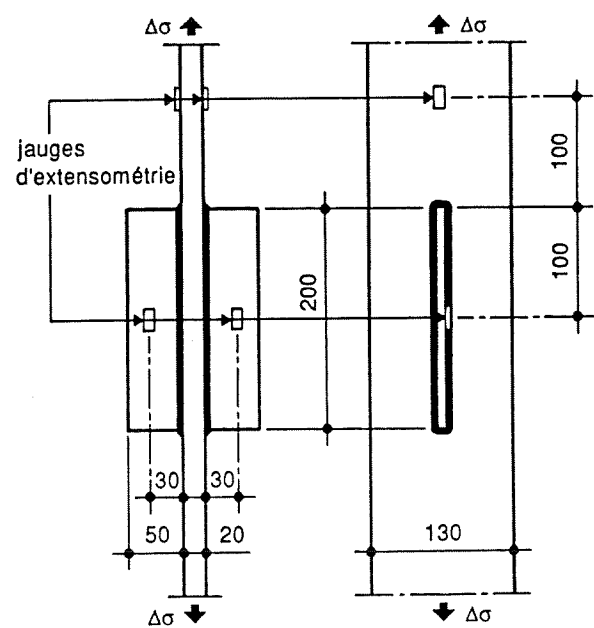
Emplacement des jauges d'extensométrie électriques collées sur les éprouvettes
